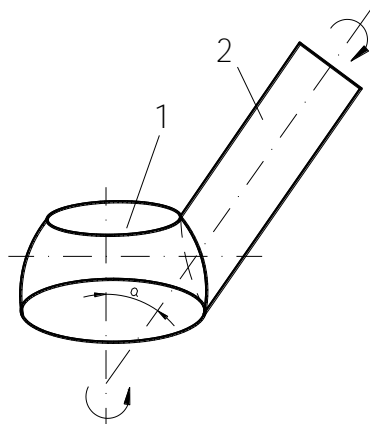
Схема обработки торических поверхностей астигматических очковых линз с помощью трубчатого инструмента
